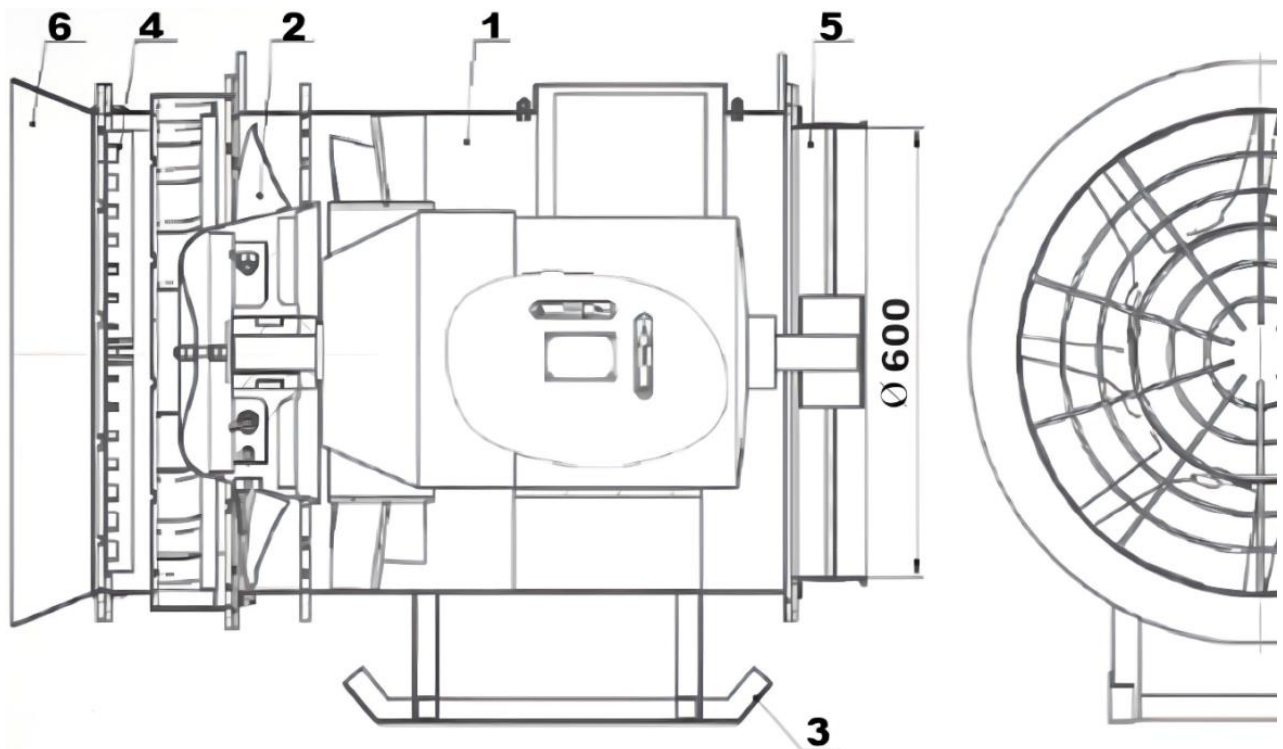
Вентилятор ВМЭ: 1 – корпус; 2 – рабочее колесо; 3 – салазки; 4 – входной патрубок; 5 – выходной патрубок; 6 – коллектор
